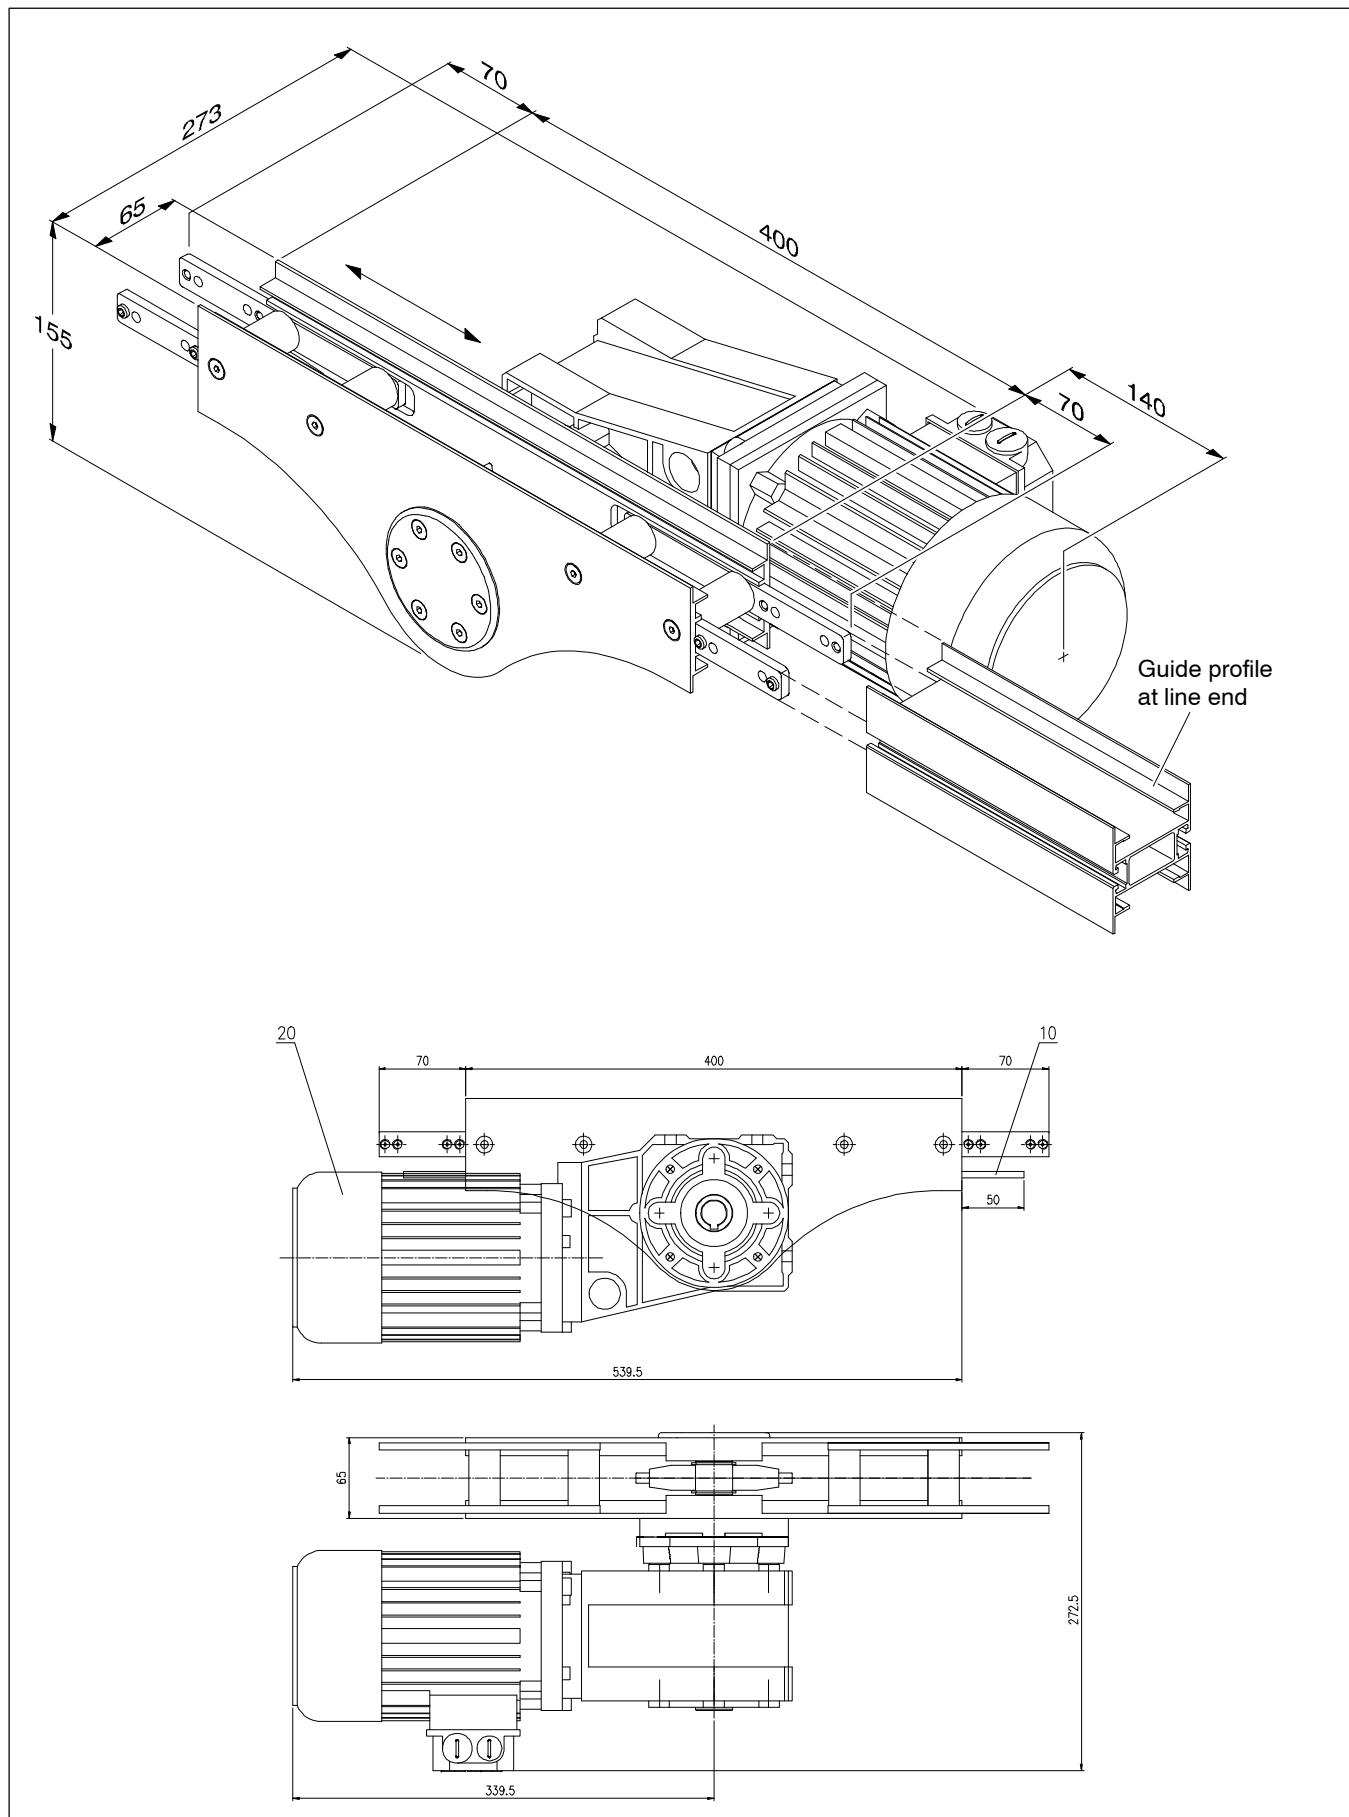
CS 065 SL direct centre drive - right-hand drive motor
